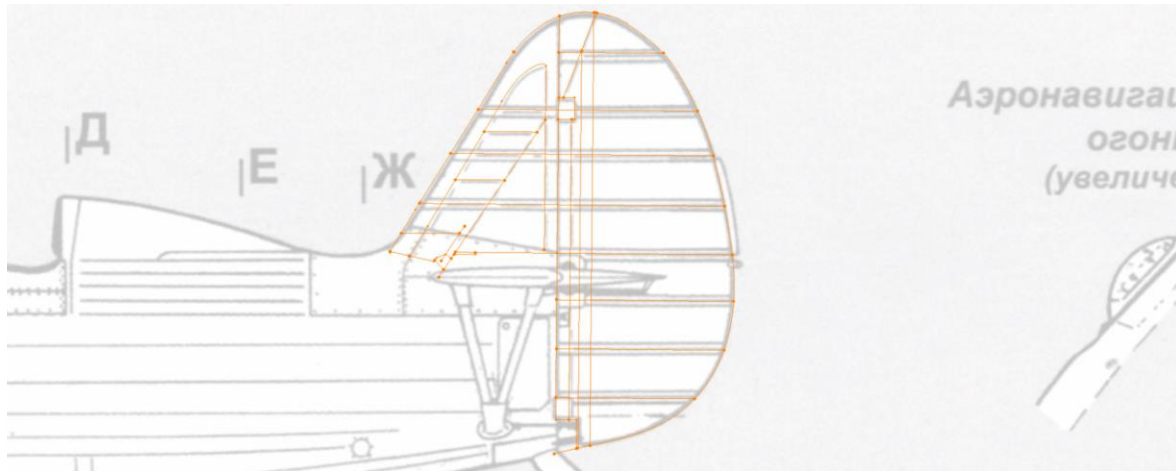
Sketch sobre el plano del estabilizador vertical
